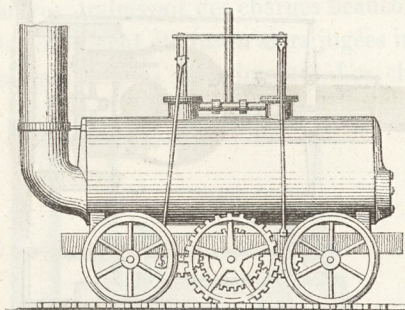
Machine à crémaillère de M. Blenkinsop.
